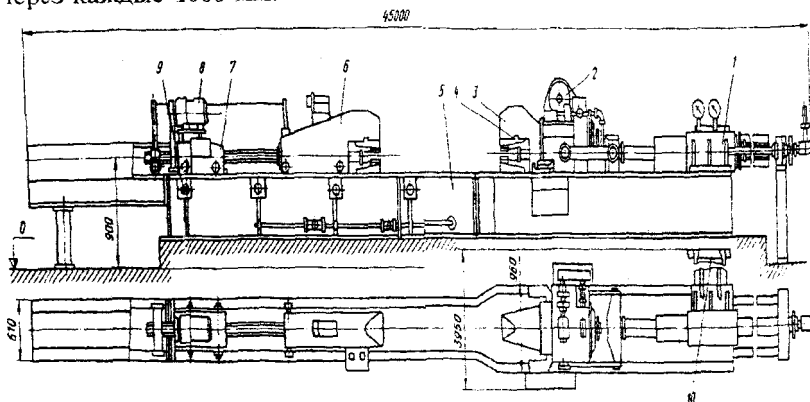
Правильно-растяжная машина усилием 0,3МН для правки и раскрутки профилей из алюминиевых сплавов: 1 - гидроцилиндр привода; 2 - механизм поворота передней головки; 3 - передняя головка; 4 - зажимные губки; 5 - станина; 6 - задняя головка; 7 - каретка; 8 - механизм перемещения задней головки; 9 - фиксатор; 10 - насосная станция
